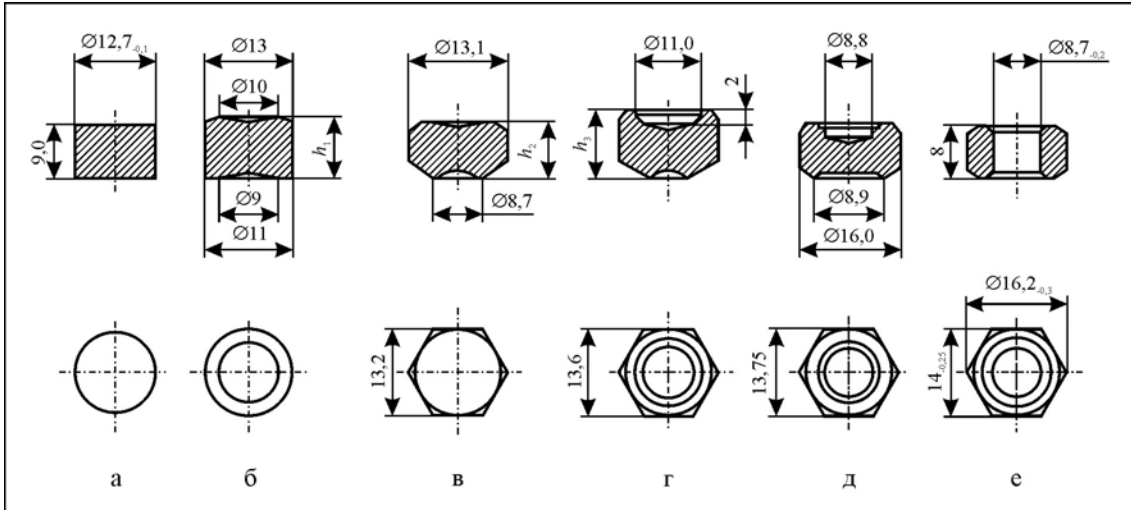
Переходи при штампуванні гайки: а – вихідна заготовка; б – перша позиція; в – друга позиція; г – третя позиція; д – четверта позиція; е – п'ята позиція
